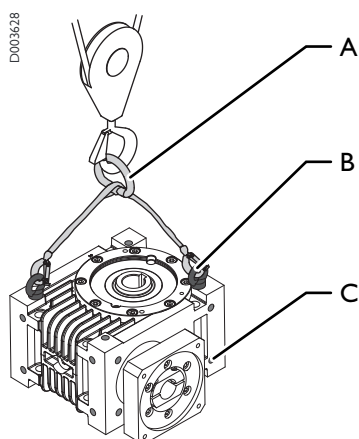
Зачаливать такелаж: Блок редуктора Güdel
